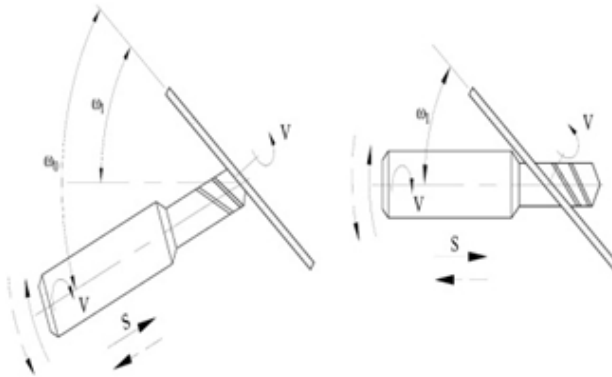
Схема изменения ориентации осей заготовки сверла и шлифовального круга методом поворота оси шпинделя заготовки.
